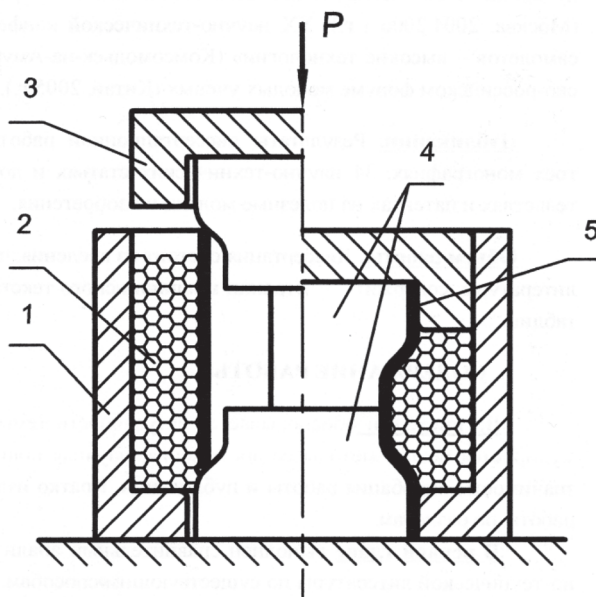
Совмещённый процесс раздачи-обжима трубной заготовки:
